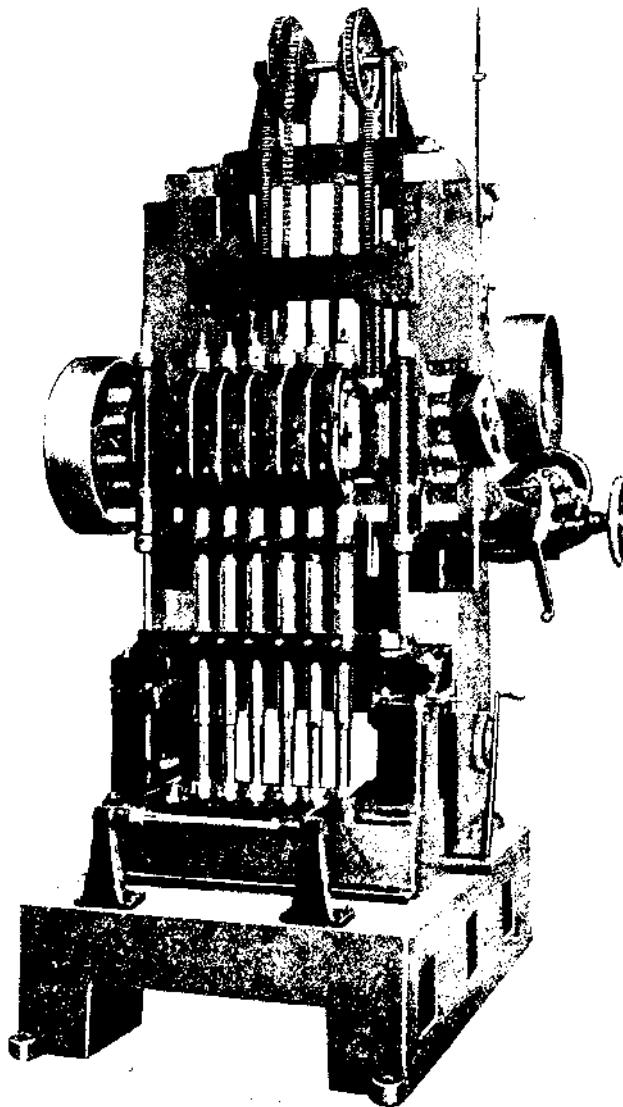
Станок Moline Tool Co с движущимися борштангами.
